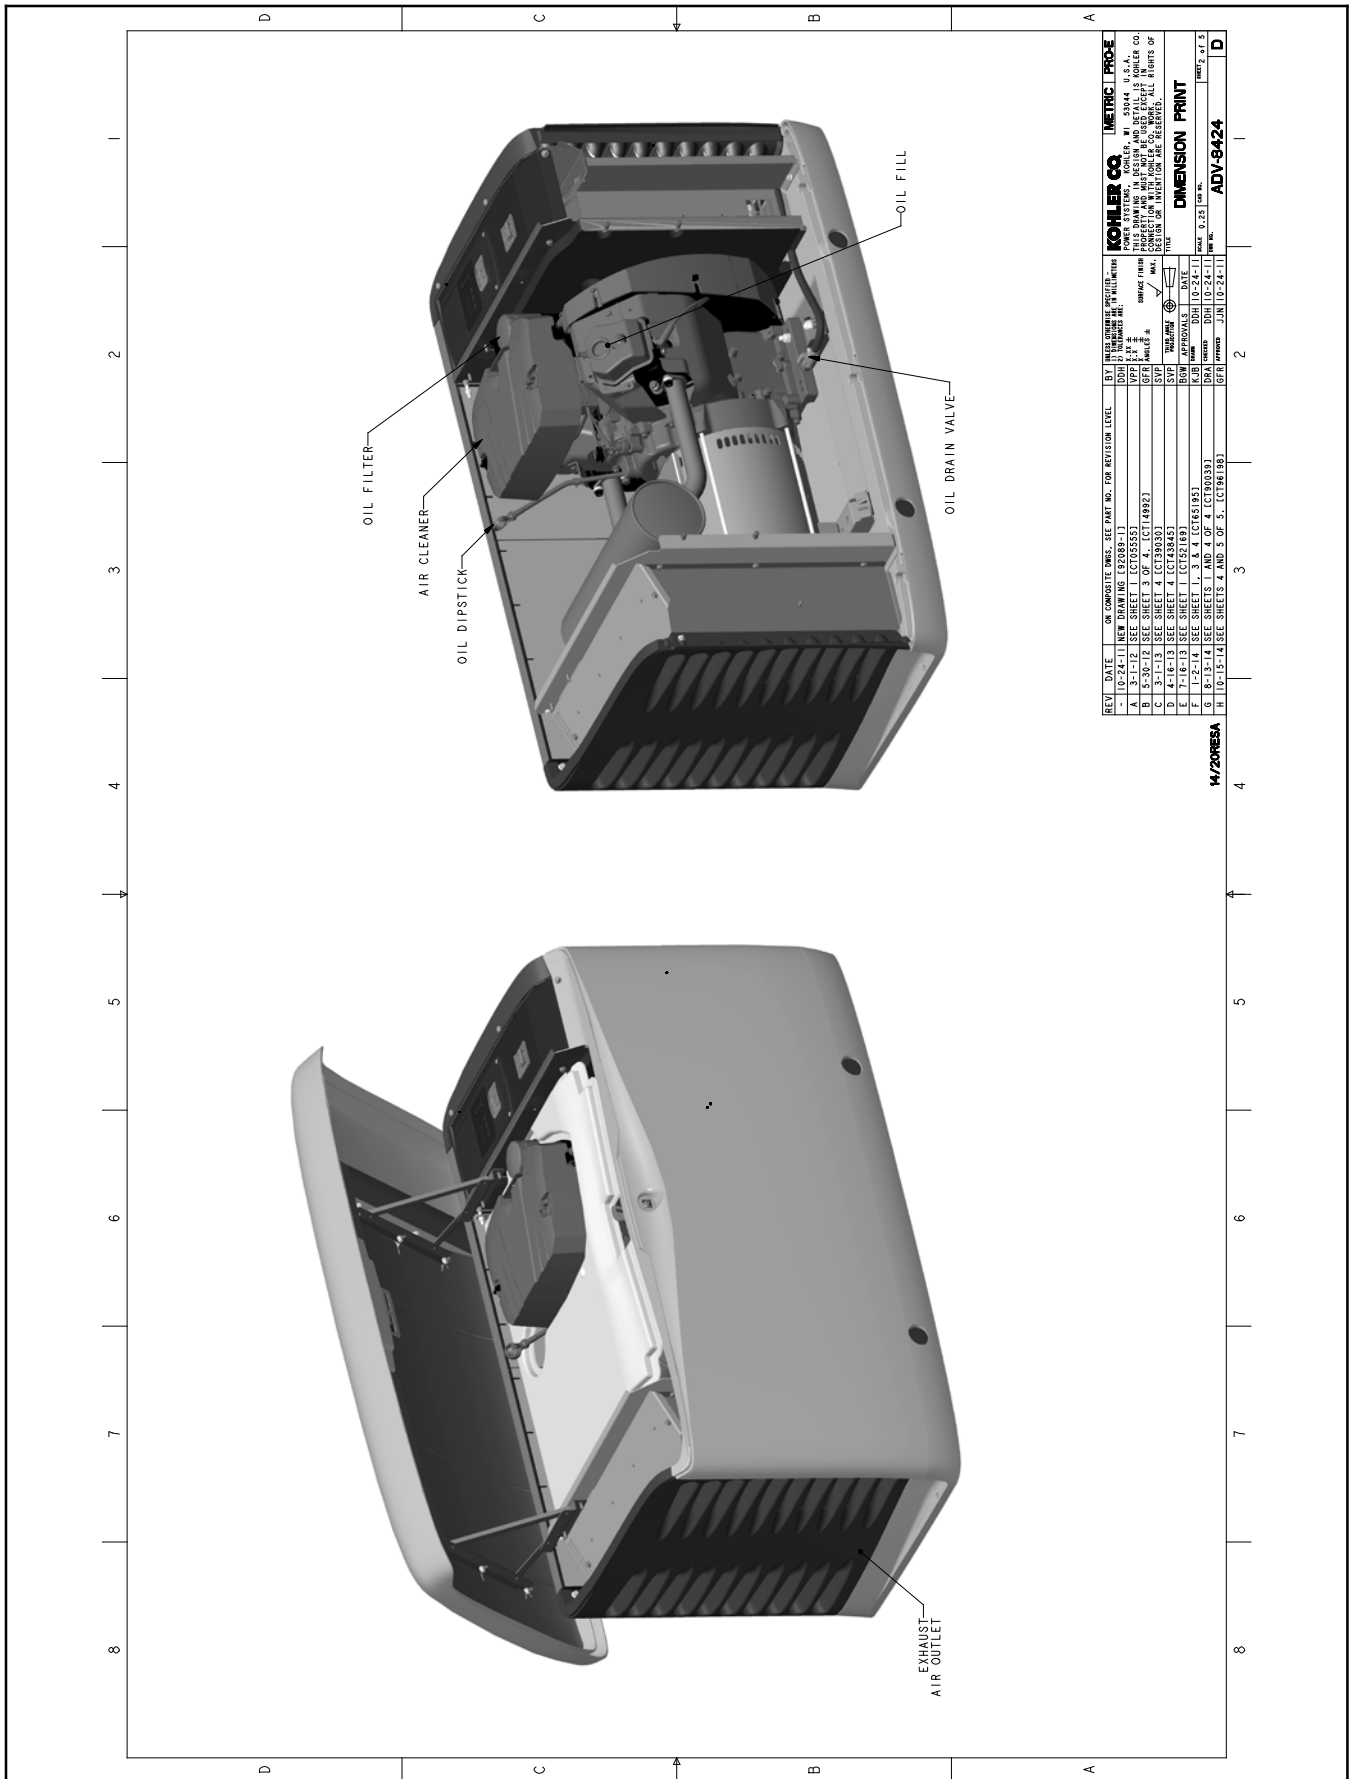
Plano acotado ADV-8424, hoja 1 de 5
